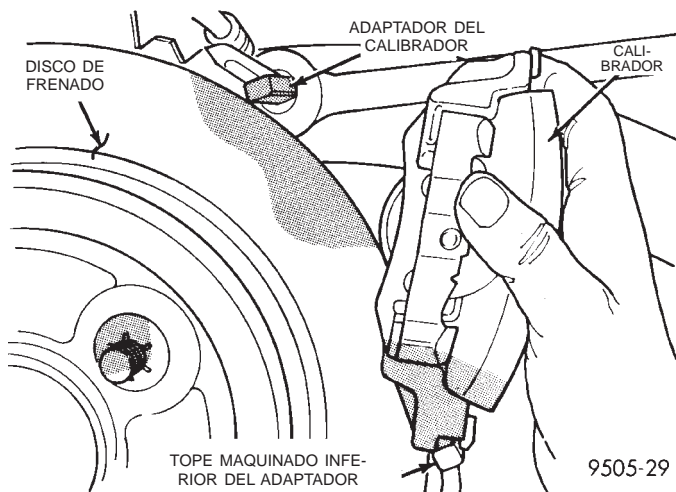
Desmontaje/Instalación del conjunto de calibrador del adaptador
